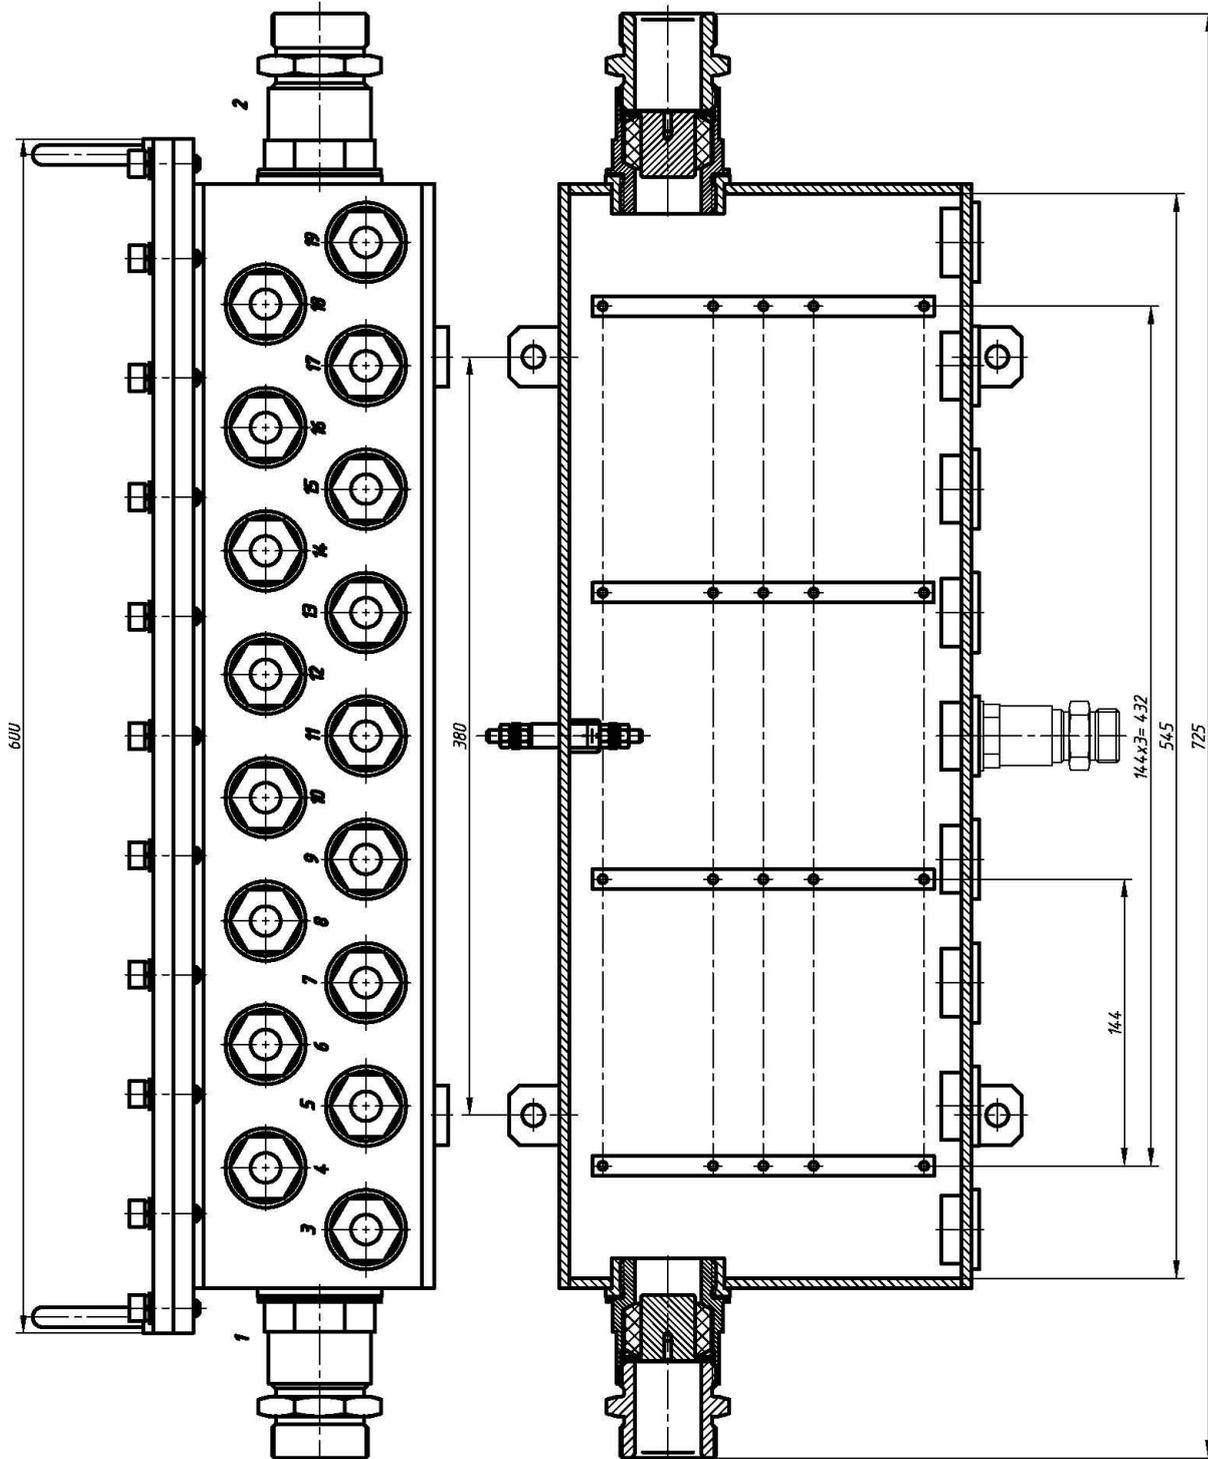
Габаритные, установочные и присоединительные размеры базовой коробки ExКСУВ-ПС600. Остальное смотреть рисунок В.1. По умолчанию в патрубках №№1 и 2 резьба G1 1/2, в патрубках №№3-19 резьба G3/4.
